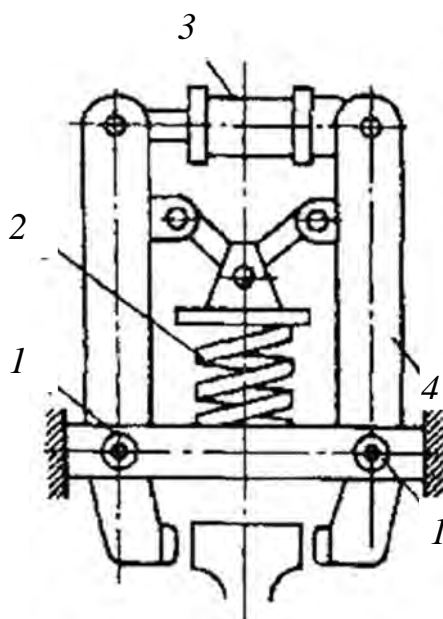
Схема механического противоугонного захвата: 1 – ось; 2 – пружина; 3 – пневмоцилиндр; 4 – рычаг механизма
